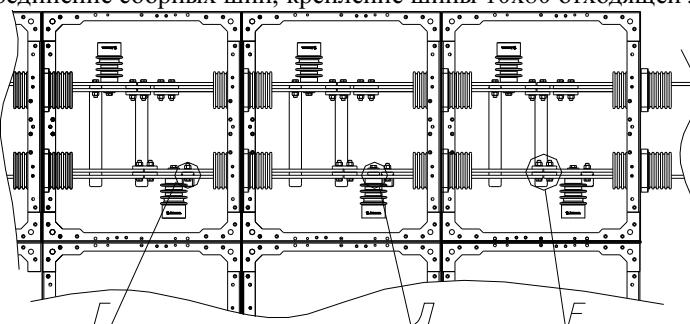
Монтаж сборных шин 1600 А (вид сверху на шкафы КРУ)
